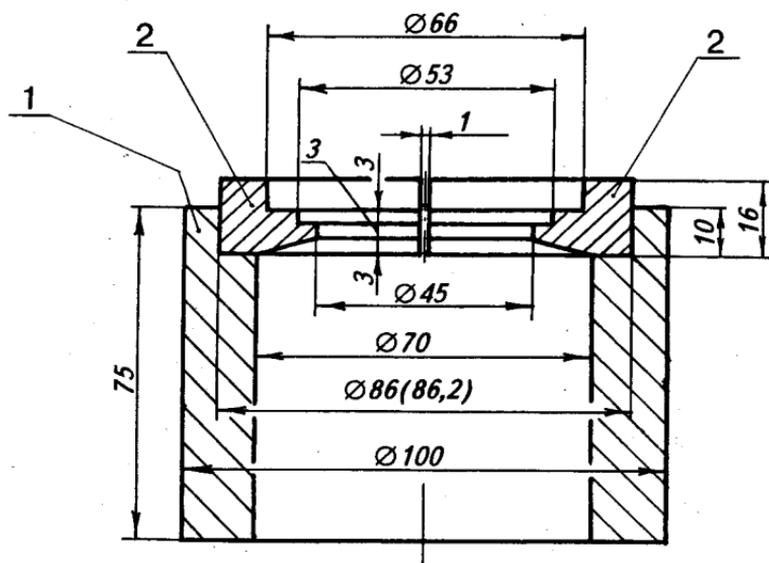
Приспособление для выпрессовывания внутреннего кольца внутреннего подшипника хвостовика: 1 — основание; 2 — полукольцо (2 шт.).
